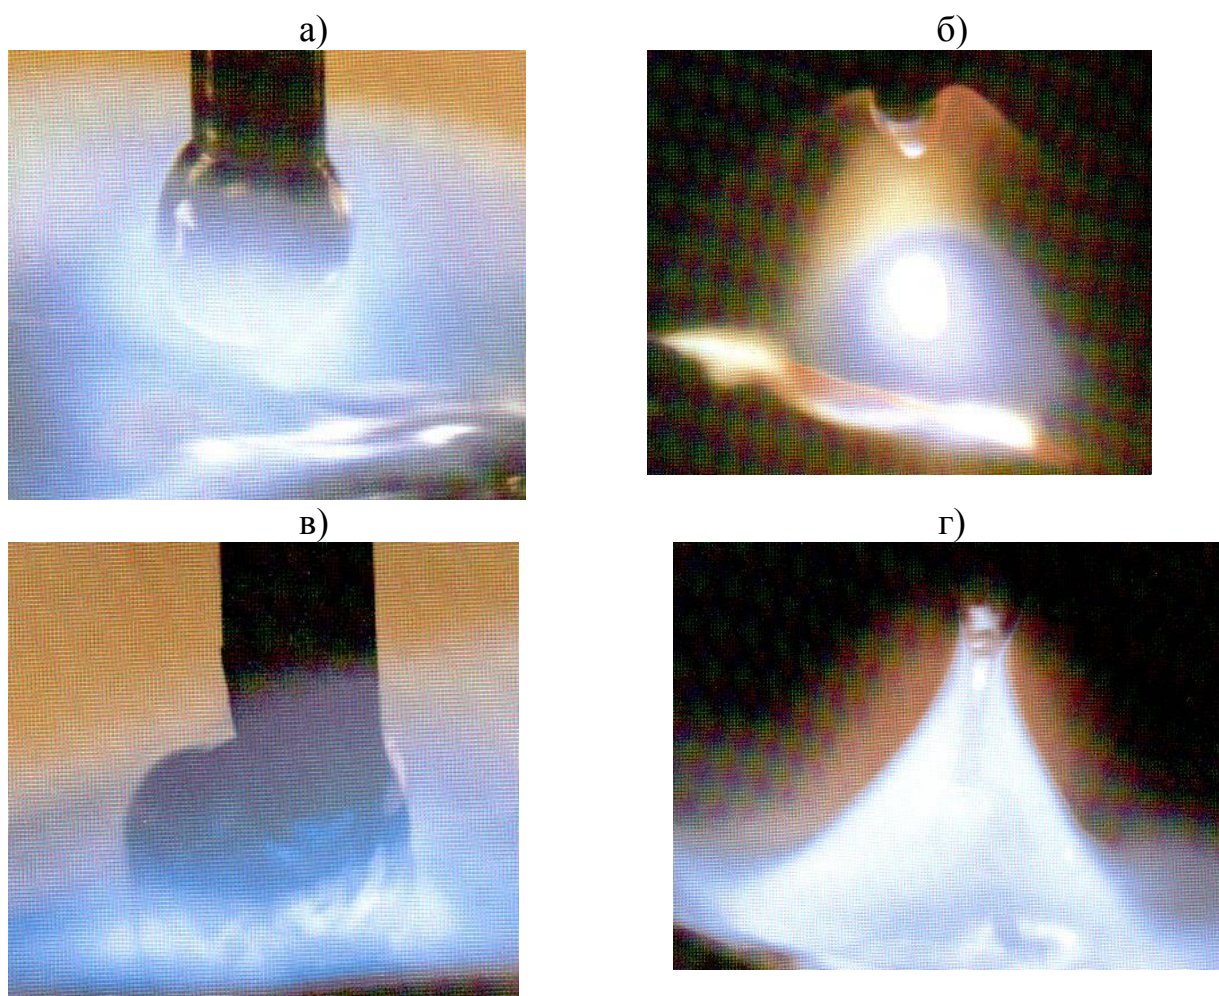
Форма горения дуги в случае различного типа переноса электродного металла: а) при сварке короткой дугой; б) при сварке импульсной дугой; в) при крупнокапельном переносе; г) при сварке длинной дугой
